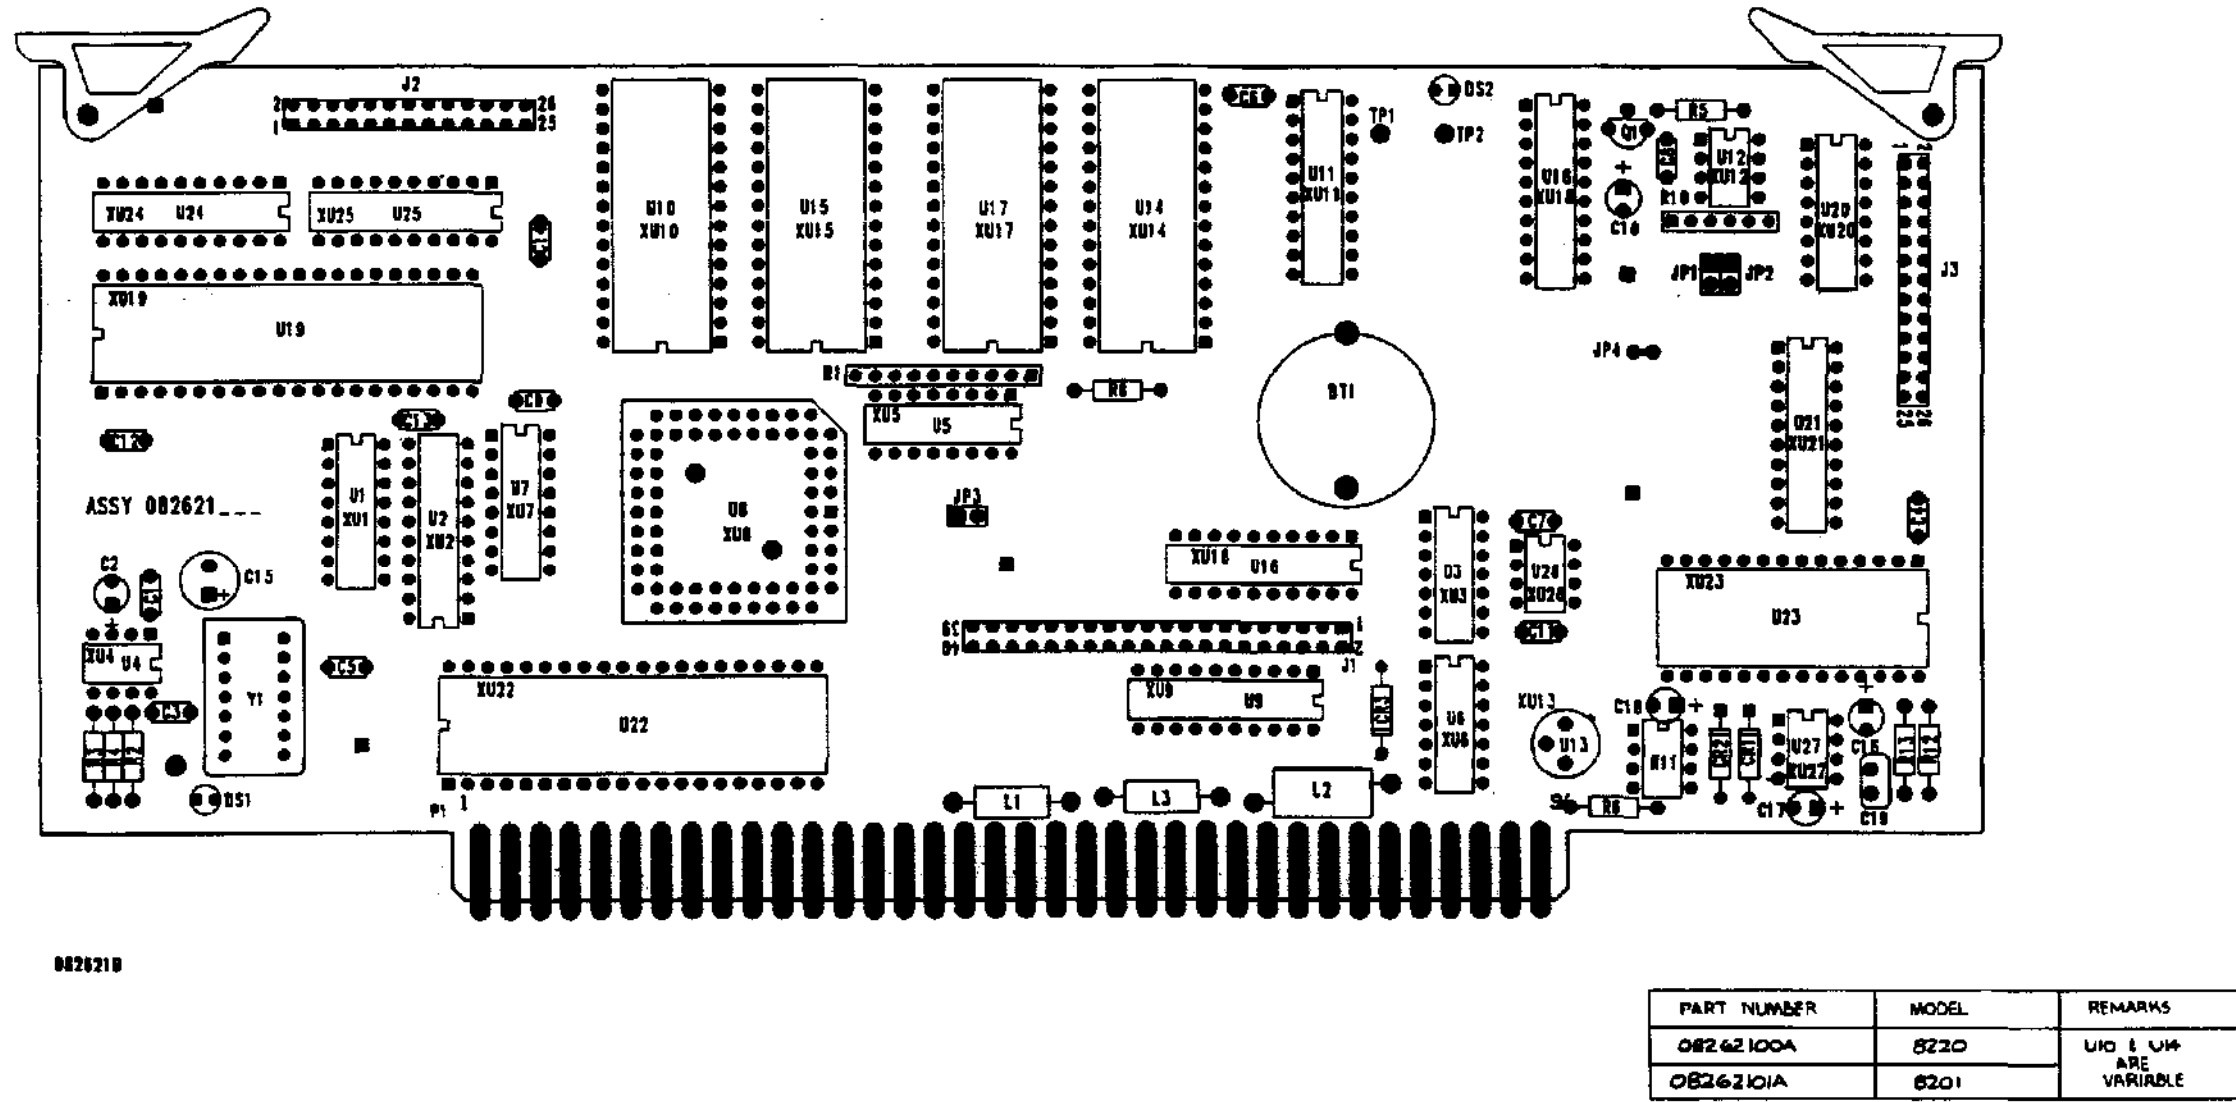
Плата ЦП А9, схема расположения деталей.
